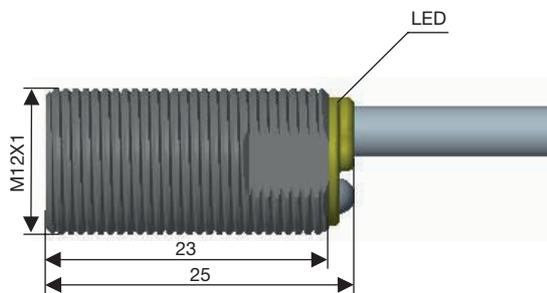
Kurze Ausführung, bündiger Einbau, Kabel
